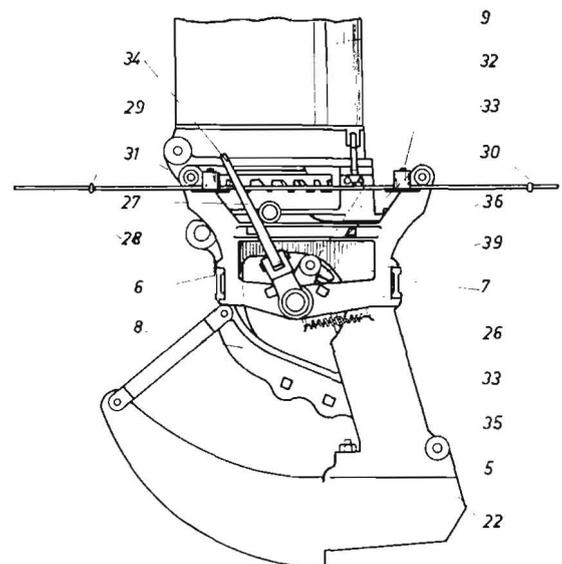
Durch einen Knotendraht gesteuerte Sämaschine
